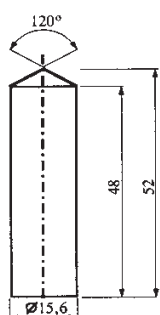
Цилиндрический бронзовый поршень; размеры в мм
